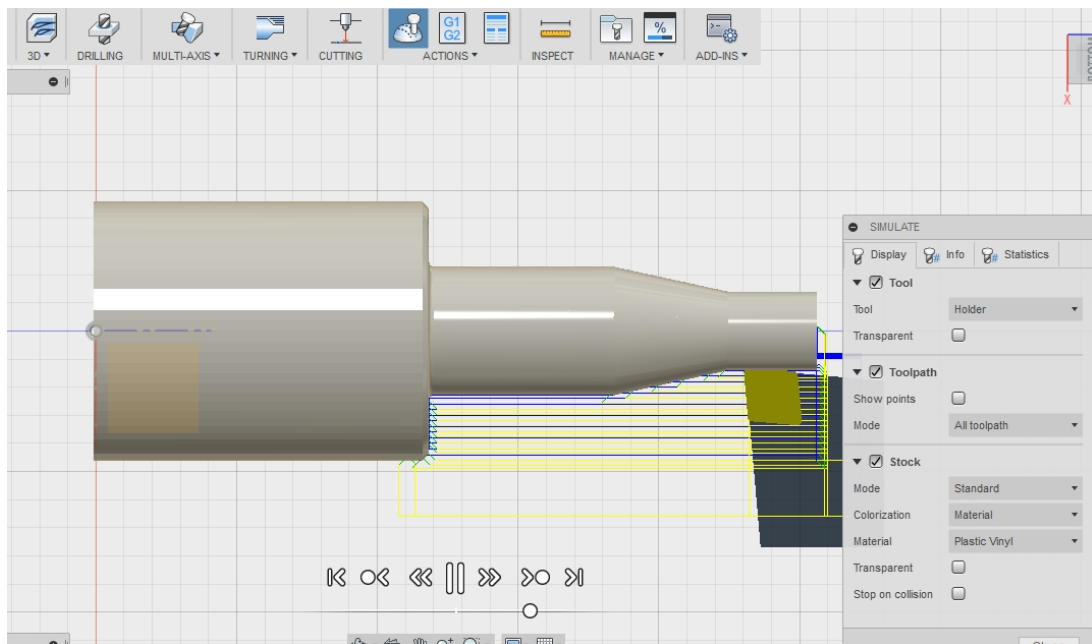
AutoCad Fusion 360 - Criação de Ferramenta
